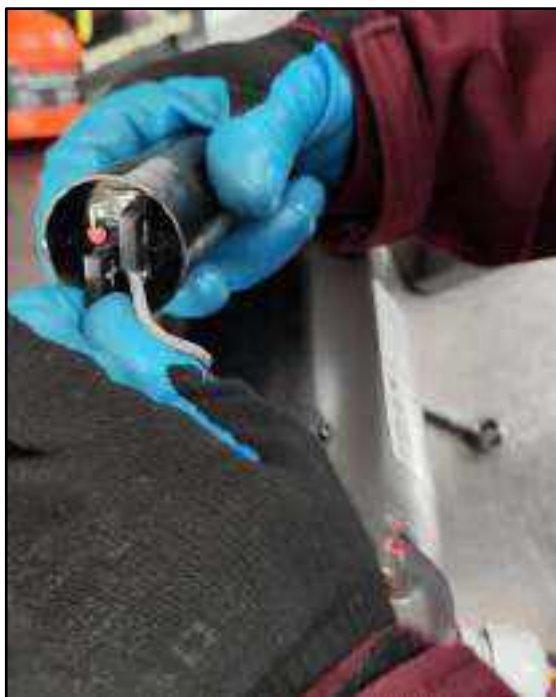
Montaje de la tapa delantera del motor
